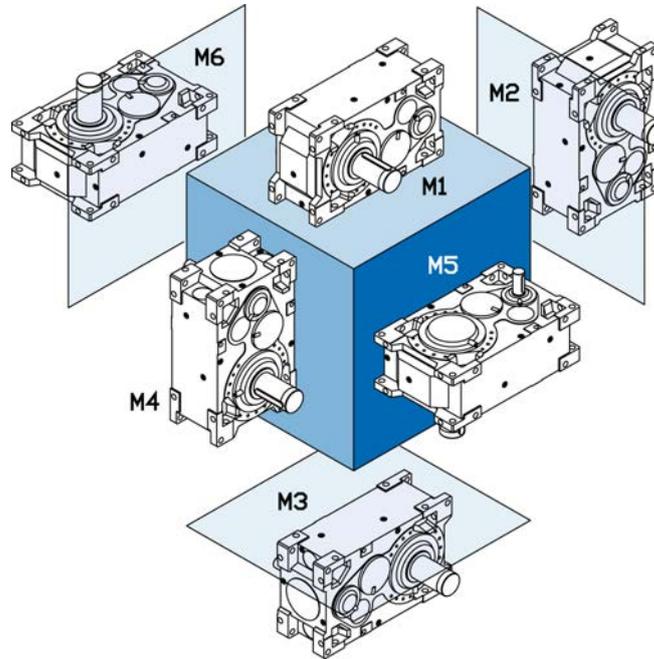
Positions de montage du réducteur à engrenages cylindriques avec surface de montage standard
